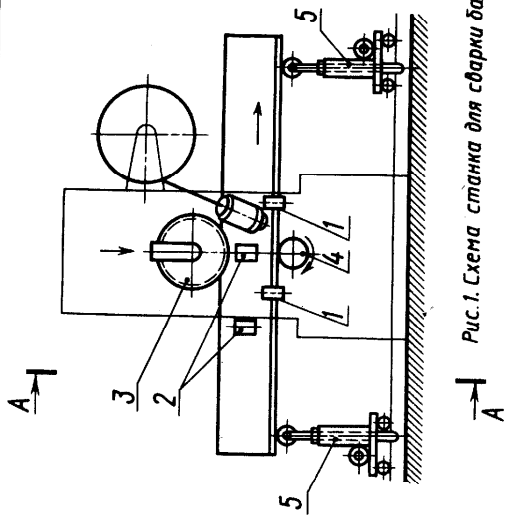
Схема станка для сварки балок табурного профиля
